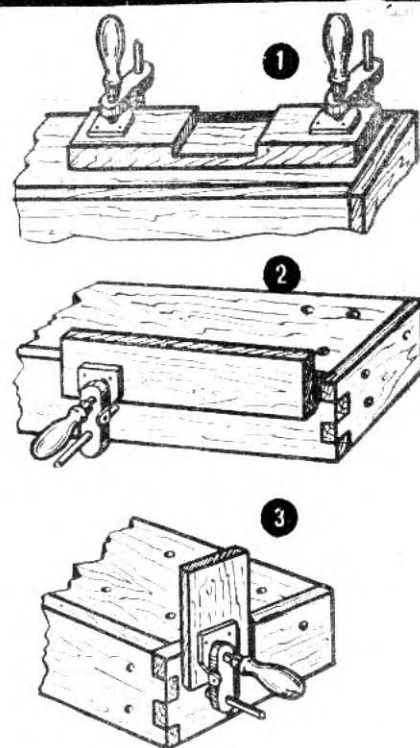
Способы крепления заготовок: 1 — строгание пластин, 2 — крепление доски на ребро, 3 — продольное пиление.
